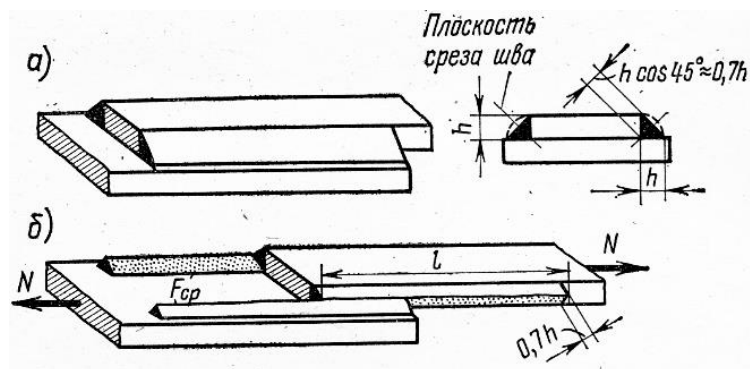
К расчету сварных соединений на срез
